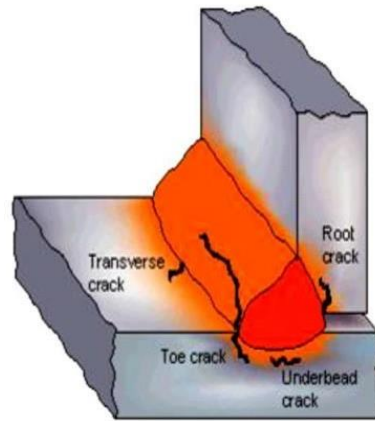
Fissuration à chaud [Dr. N. BOUMECHRA, 2011].
